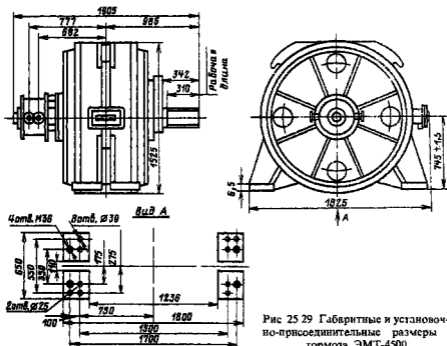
Габаритные и установочно-присоединительные размеры тормоза ЭМТ-4500
